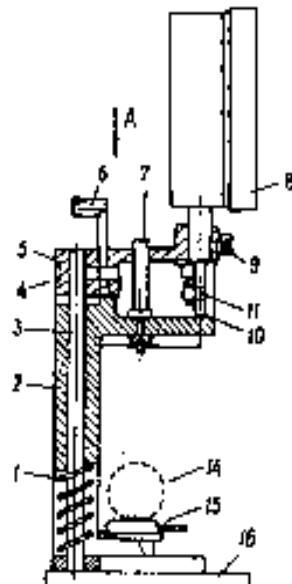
Пристрій КИ-9918 : 1-пружина; 2- каретка; 3-напрямна; 4-вісь; 5-корпус; 6- відтискний ковпачок; 7-стержень; 8-індикатор; 9-важіль; 10-кулачок гальма; 11-пластичні пружини; 12-гвинт; 13-стопорний гвинт; 14-валик декомпресора; 15-коромисло; 16-тарілка пружини клапана.
